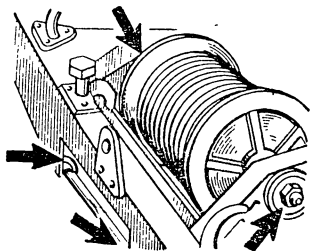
Подшипники лебедки, смазываемые смазкой УСс-2 или УСс-1 (4 точки, автомобиль ГАЗ-63А)
